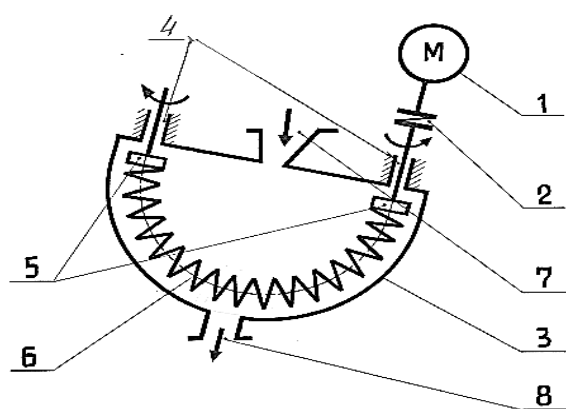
Схема пружинной мельницы для сверхтонкого помола
